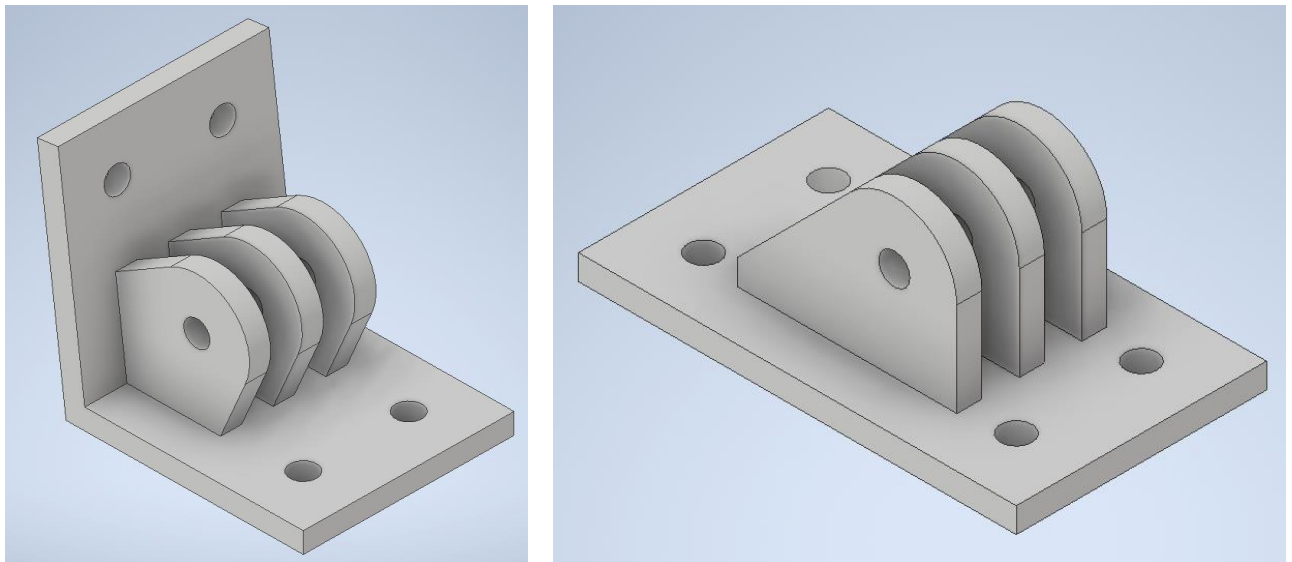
Uniones barra de apoyo (izquierda) y barra principal (derecha) con la cubierta.
